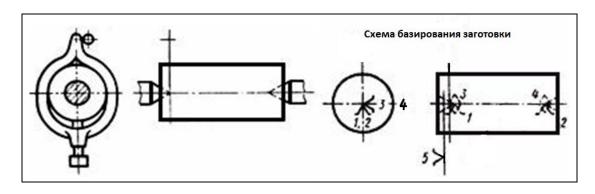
Установка вала в центрах на конические поверхности центровых гнезд
